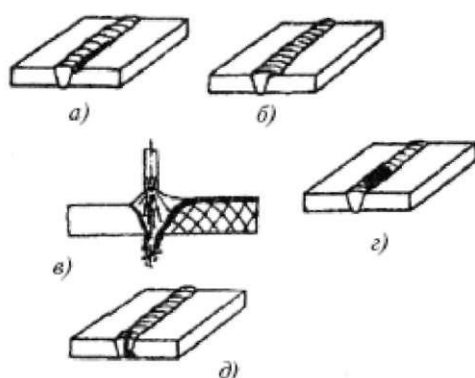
Наружные дефекты сварных швов, выявляемые внешним осмотром: а - подрез; б - наплыв; в - прожог; г - незаваренный кратер; д - свищ
